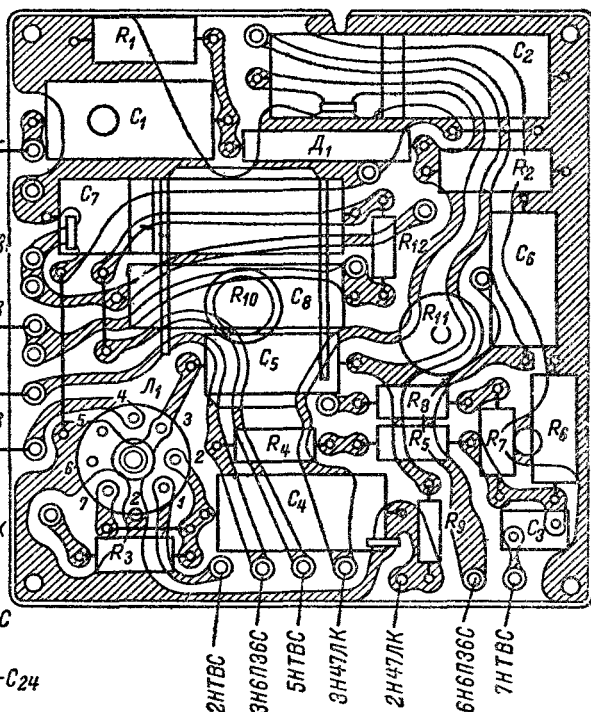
Расположение деталей на печатных платах блока 3 (амплитудный селектор; задающий генератор и выходной каскад кадровой развертки, фазоинверсный каскад, задающий генератор и схема АПЧиФ строчной развертки) и блока 4 (схемы стабилизации размера изображения и гашения обратного хода луча) телевизора УНТ-47-III.
